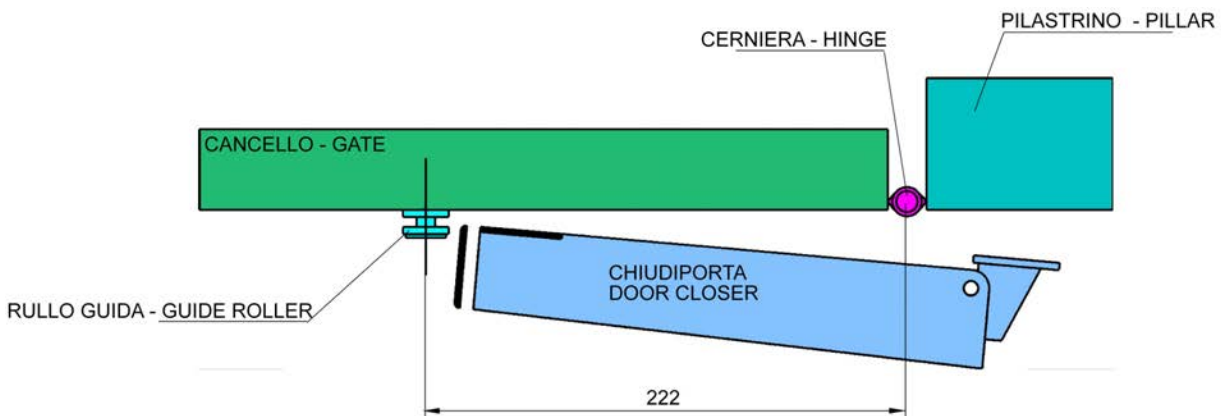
Fissaggio del rullo guida - Fixing the roller guide
